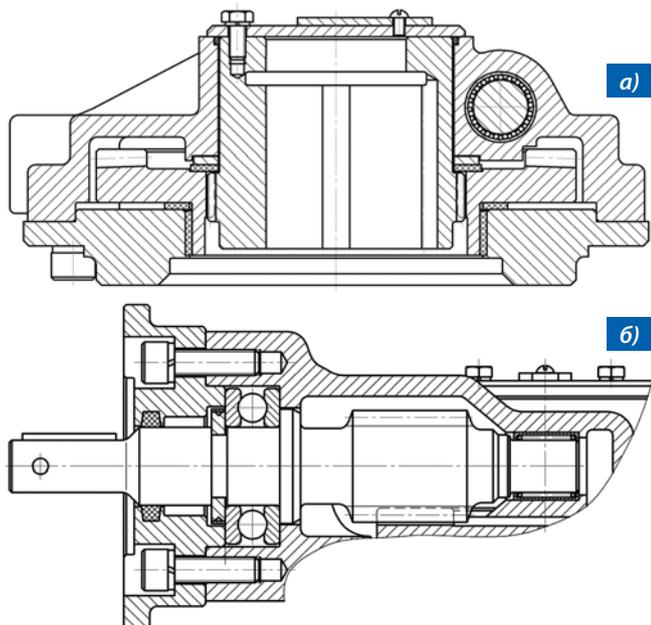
Типовая конструкция узла колеса (а) и узла червяка (б) спироидного редуктора ТПА
